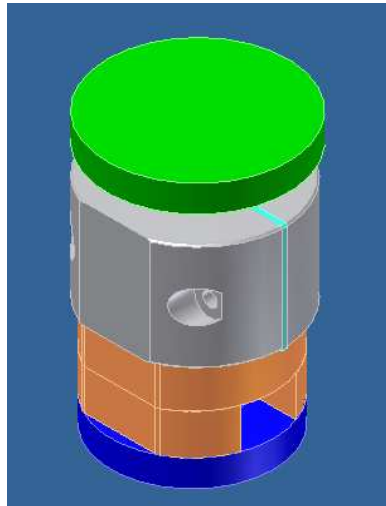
Molde de blocos montado em posição de compressão da peça.
